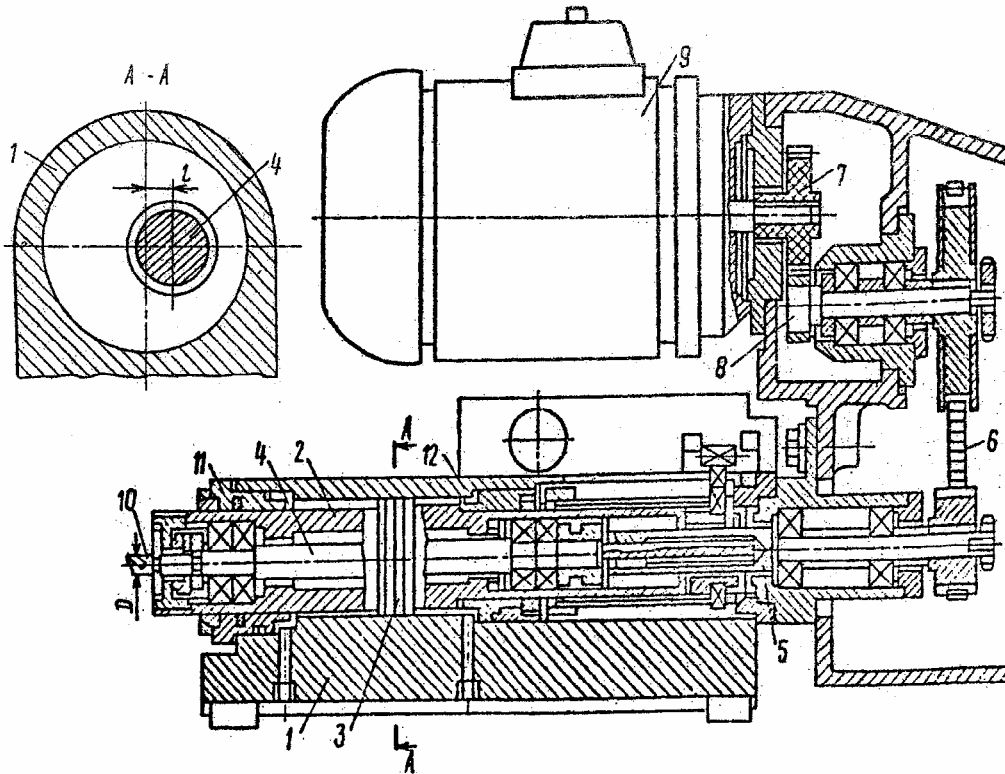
Силова головка з ексцентричним розташуванням шпинделя і штока циліндра подачі
